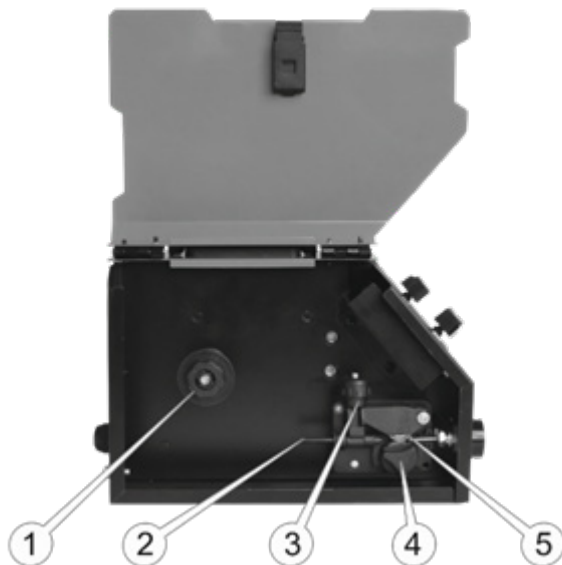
Схема встановлення котушки зі зварювальним дротом.
